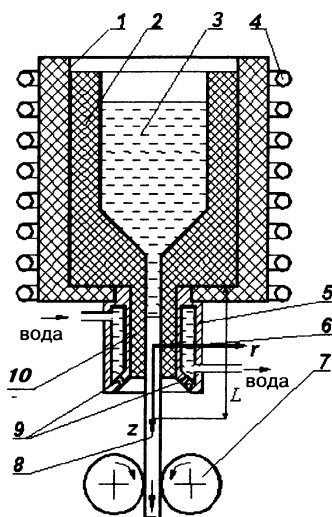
Схема непрерывного литья проволочных заготовок: 1 — футеровка; 2 — тигель; 3 — расплав; 4 — индуктор; 5 — металлический корпус; 6 — охлаждающая вода; 7 — вытягивающее устройство; 8 — отливка; 9 — отверстия вторичного охлаждения; 10 — рабочая втулка кристаллизатора
